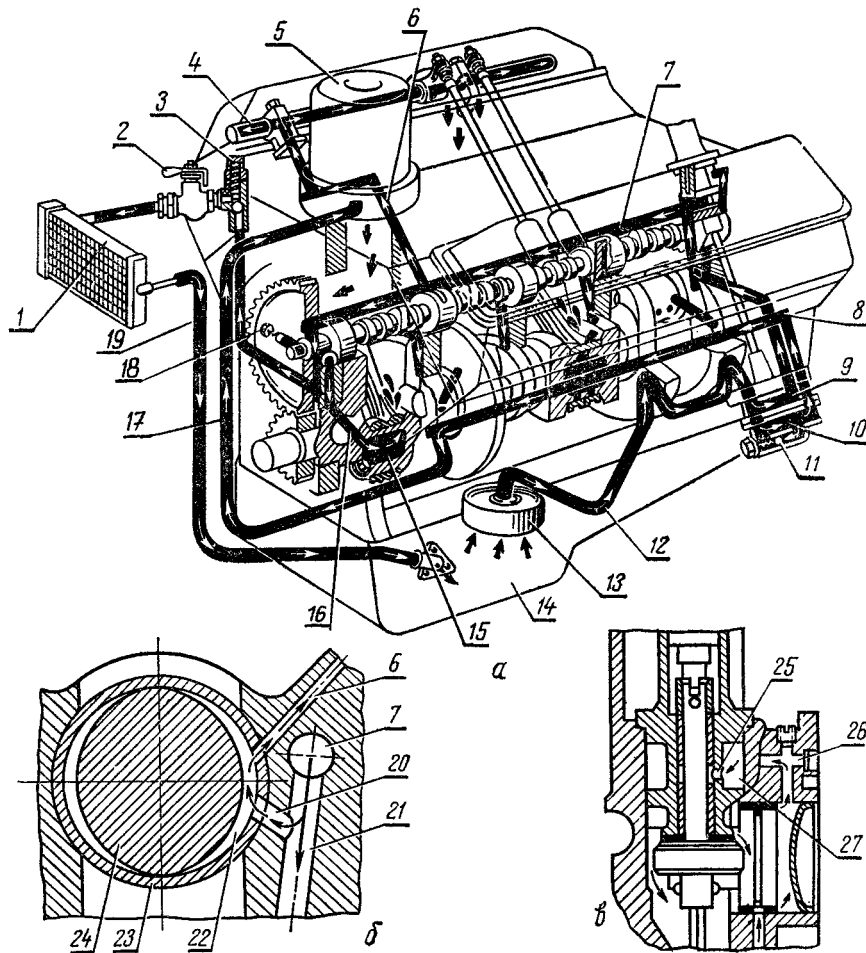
Схема системы смазки двигателя ГАЗ-53:
